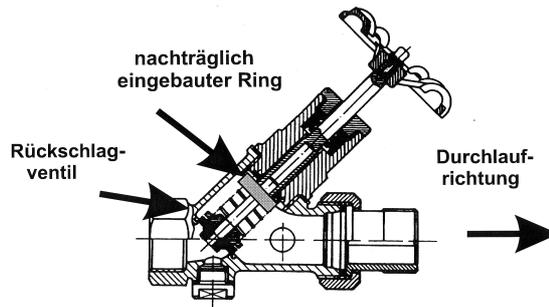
Schrägsitzabstellventil mit Rücklaufsperrre umgebaut als Gleichdruckregelung
